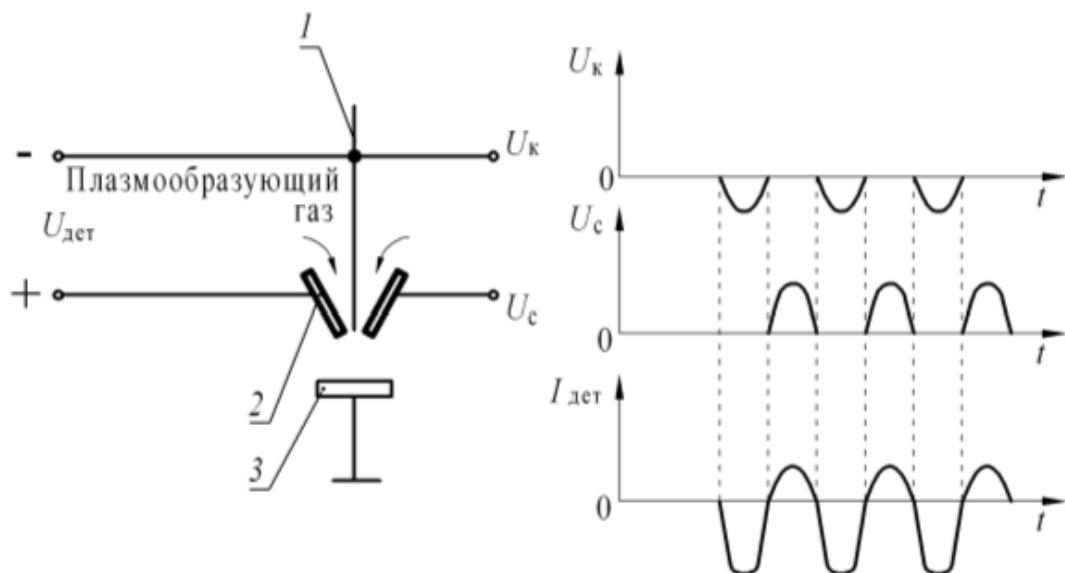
Схема, иллюстрирующая принцип микроплазменной сварки на переменном токе:
